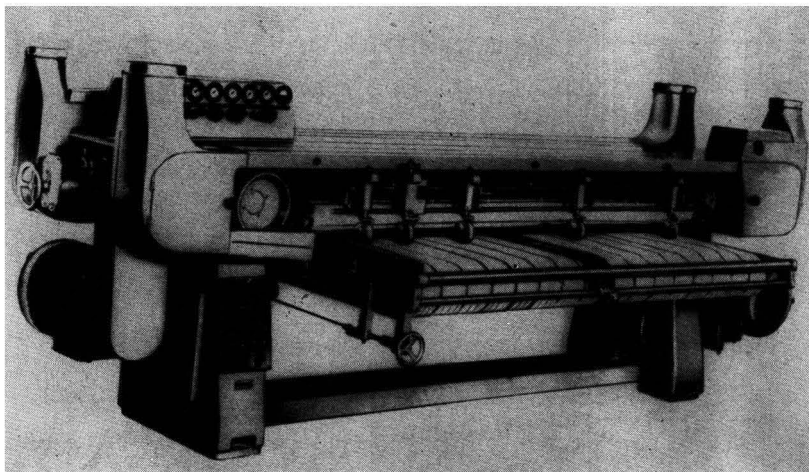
Ленточно-шлифовальный станок проходного типа
